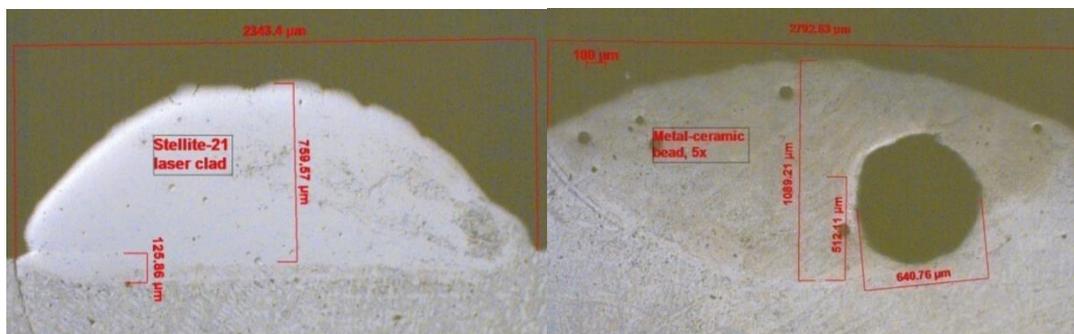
Поперечное сечение валика при наплавке из порошка (а) стеллита-21 и (б) металлокерамических порошков
